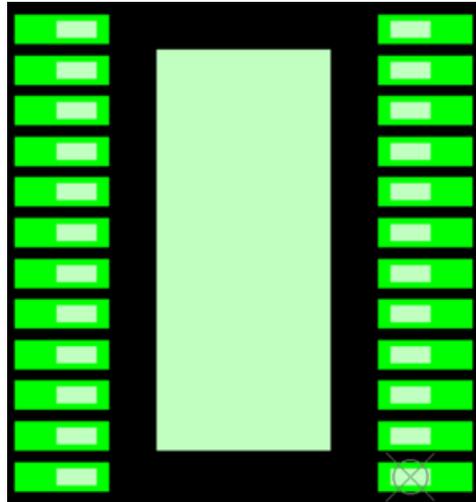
PWP0024T PCB パッドの SO-24、白 : その他の SO-24 リード、緑 : TI PWP0024T PCB パッド
